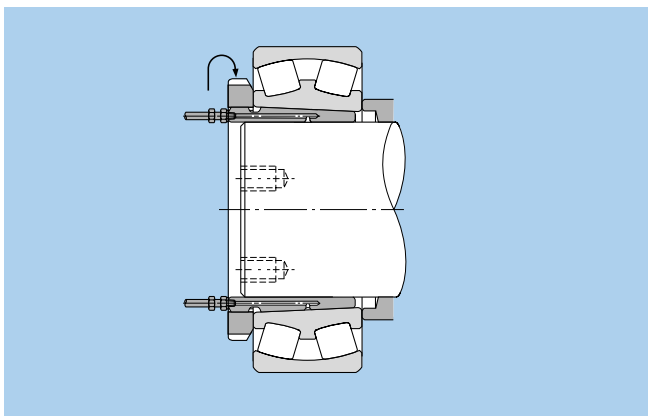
Extração utilizando uma bucha hidráulica de desmontagem
